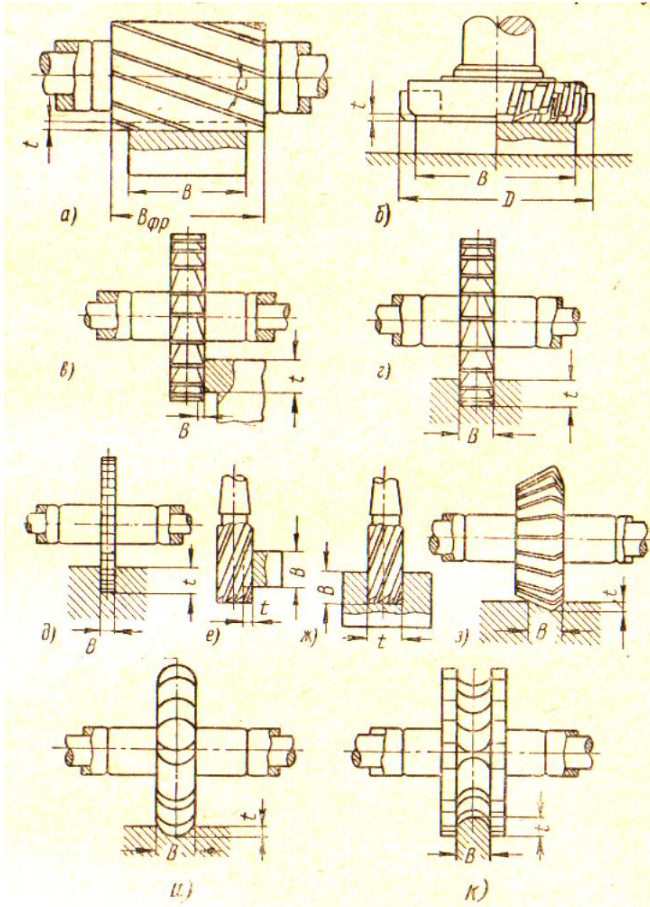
Основные типы фрез: а- цилиндрические, применяются для обработки открытых плоскостей; б – торцовые – имеют зубья на цилиндрической и торцевой поверхностях, применяют для обработки открытых плоскостей; в, г, д – дисковые фрезы применяют для обработки уступов, пазов, лысок, многогранных и других боковых поверхностей на прямоугольных и круглых заготовках (могут быть одно-, двух – и трёхсторонними: в, г, односторонняя дисковая фреза имеет режущие кромки только на цилиндрической части- прямозубая) ; г – прорезные и отрезные применяют для прорезки узких пазов (шлицы винтов и др.) и отрезки заготовок; е, ж – концевые фрезы применяют для обработки плоскостей, уступов, пазов и криволинейных контуров по разметке и копиру; з – угловые фрезы применяют для обработки поверхностей, расположенных под некоторым углом; и, к – фасонные фрезы применяют для изготовления сложно-фасонных поверхностей.
